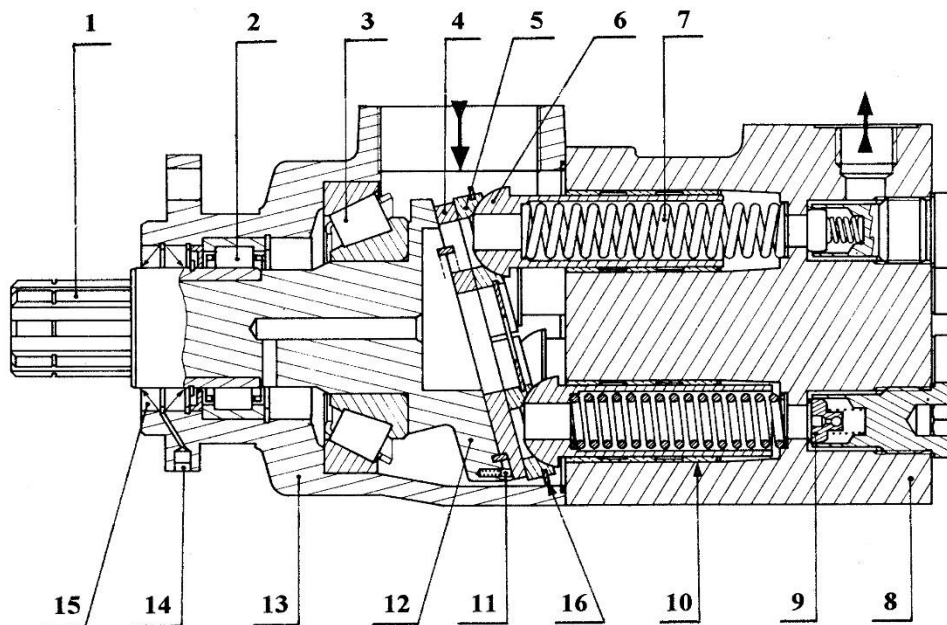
Dessin d'ensemble de la pompe hydraulique à pistons axiaux.
